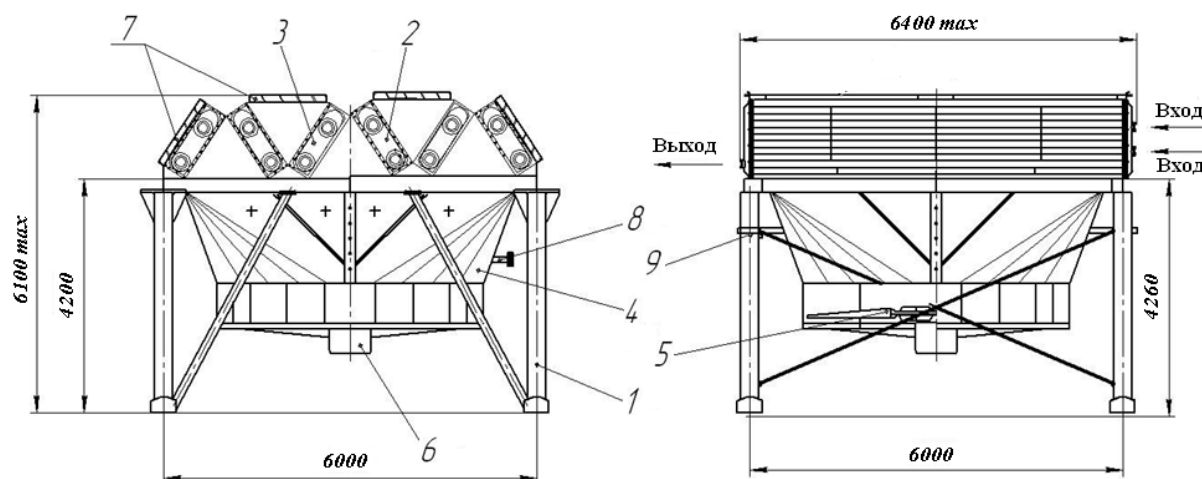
Общий вид аппарата АВЗ [5]:
